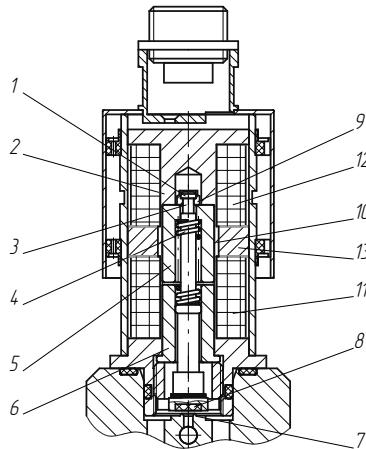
Конструктивна схема пневматичного клапана з двопозиційним поляризованим електромагнітним приводом: 1 – головка штока; 2 – корпус електромагніта (верхній стоп); 3 – шийка штока; 4 – буферна пружина; 5 – повзун (якір); 6 – нижній стоп; 7 – сідло; 8 – золотник; 9 – стопорна шайба; 10 – трубка розподільна; 11 – обмотка закриття; 12 – обмотка відкриття; 13 – постійний магніт
